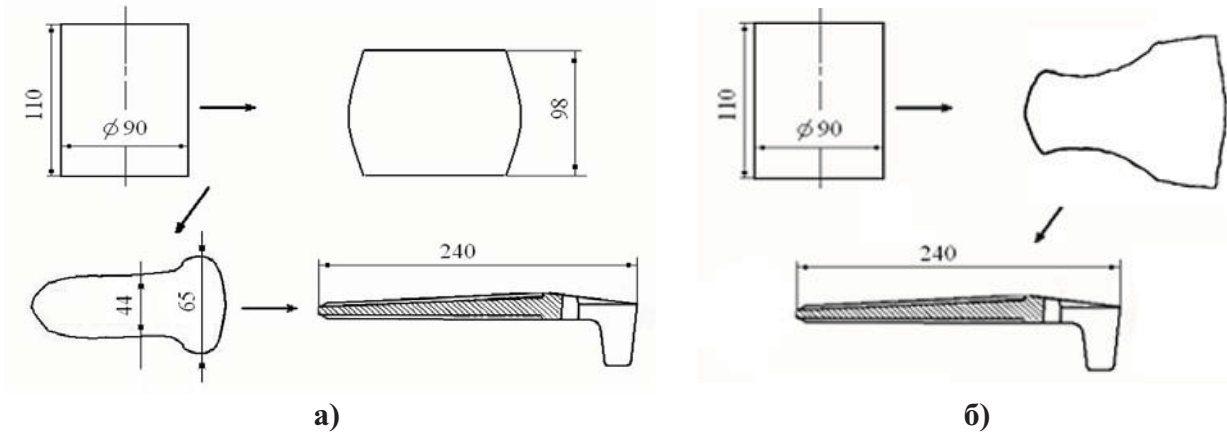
Эскизы переходов штамповки поковки «Пластина подвижная»:
